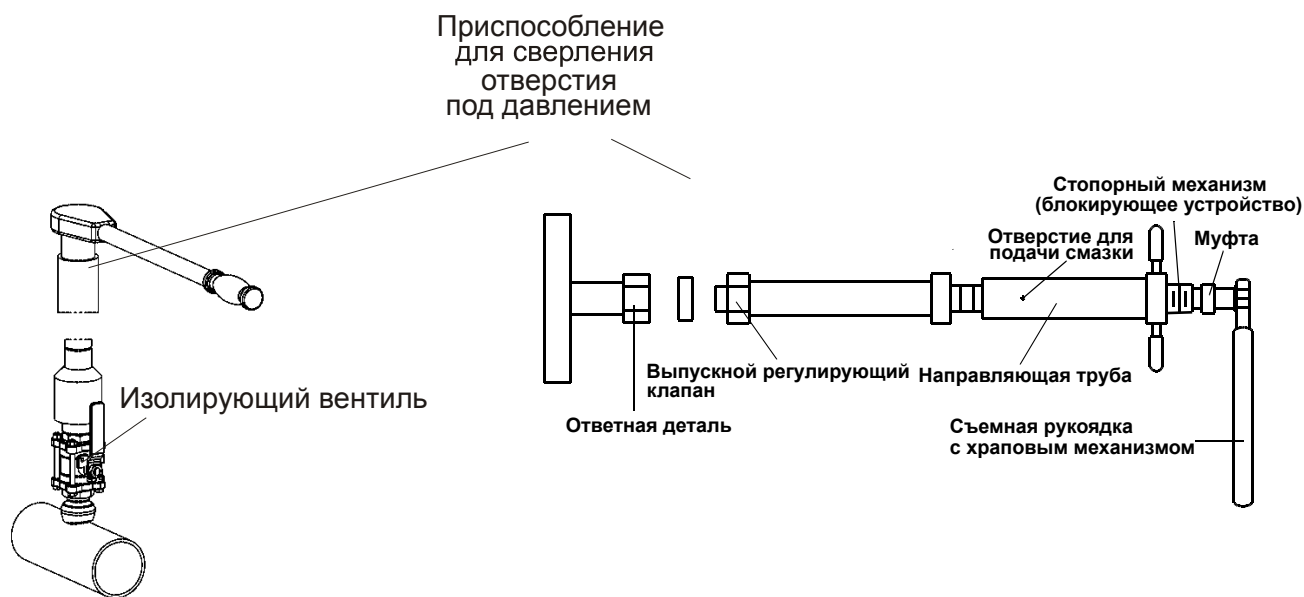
Приспособление для сверления отверстия под давлением на изолирующем вентиле
